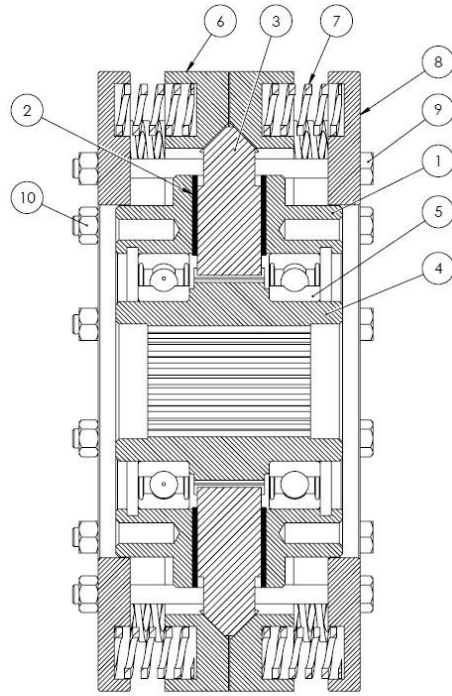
Aşırı Yük Kavramasının 3D Montaj Resmi.
